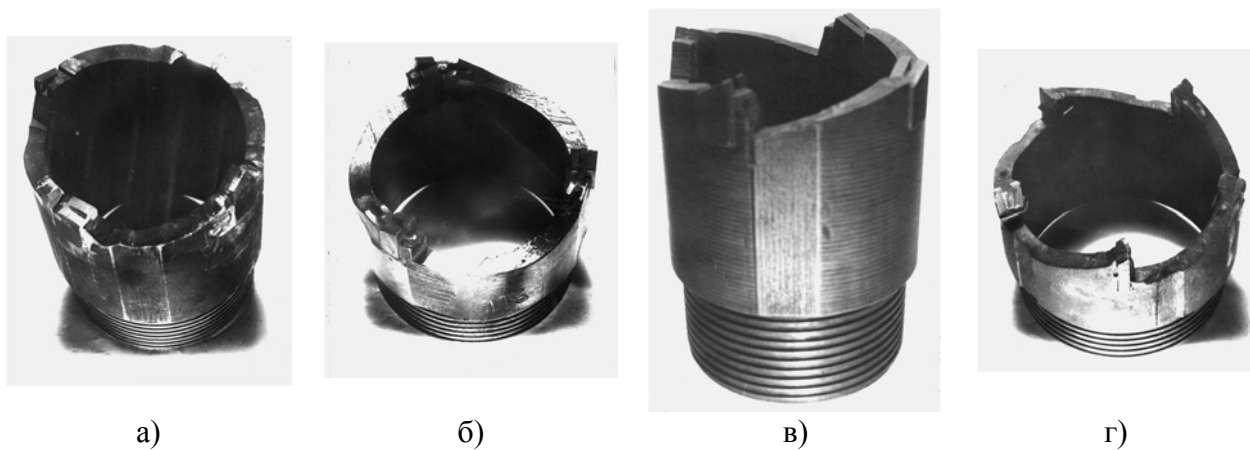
Породоруйнівний інструмент нової форми для колонкового буріння – твердосплавні коронки типа ТКД -2 (а), ТКД – 3 (б), ТКД-4 (в), СТК (г)
